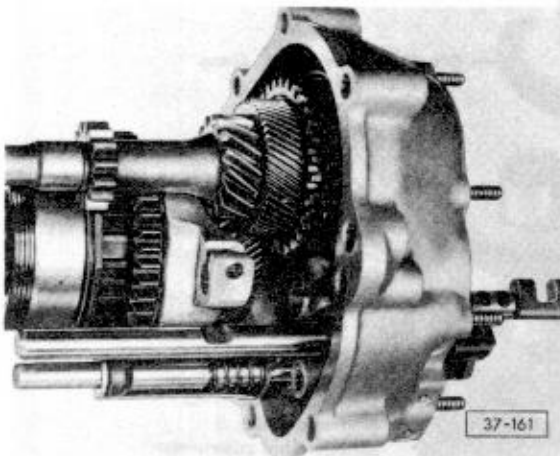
Klemmschraube für Schaltgabel 2. + 3. Gang heraus-schrauben und Schaltstange zurück-ziehen
